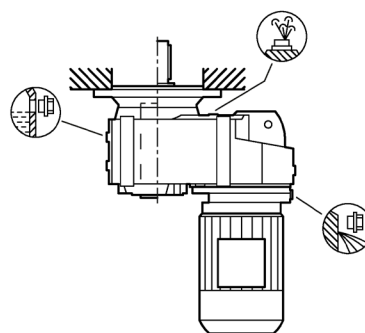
Einbautagen für Flachgetriebe F.F Flanschausführung und F.Z mit Gehäuseflansch, Baugröße 29
